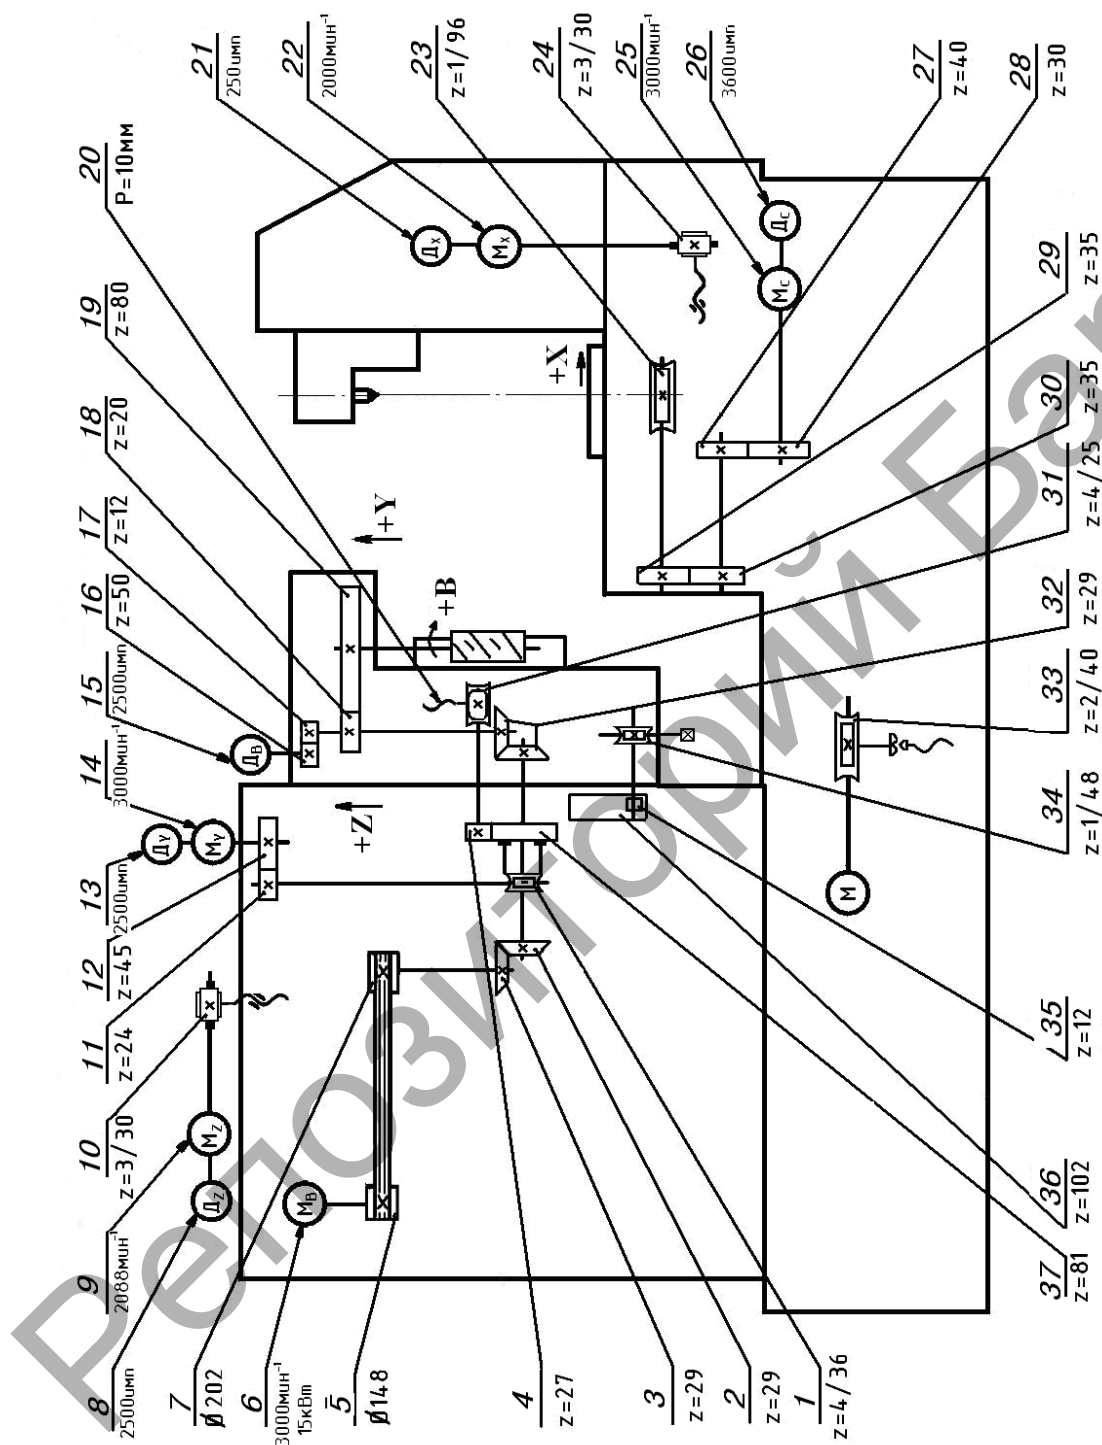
Кинематическая схема станка модели 53A50KF4
